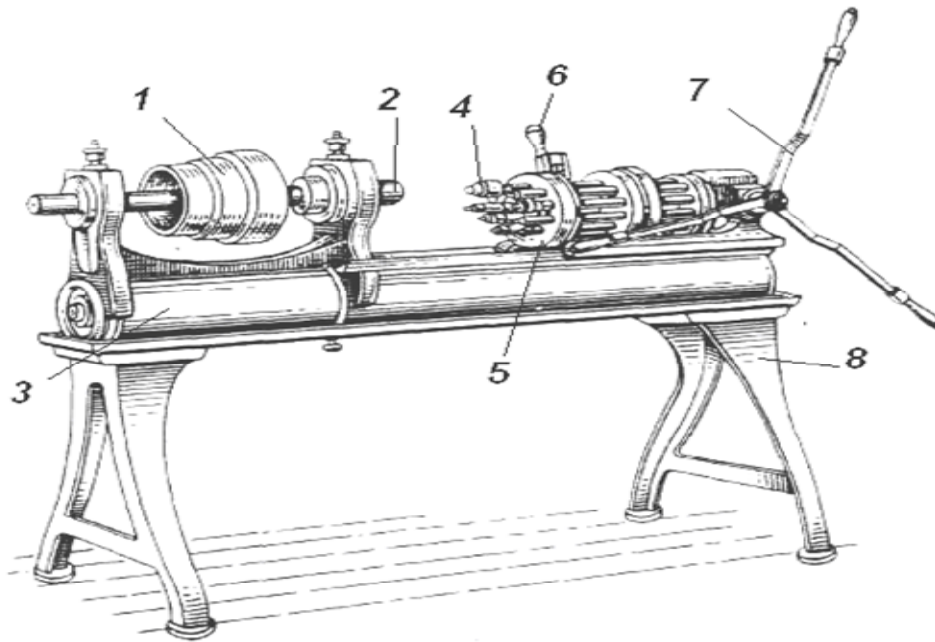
Токарно-револьверный станок 1850 г. (США):
